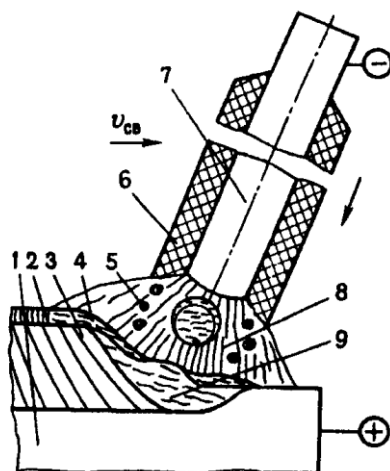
Схема процесса сварки металлическим покрытым электродом
